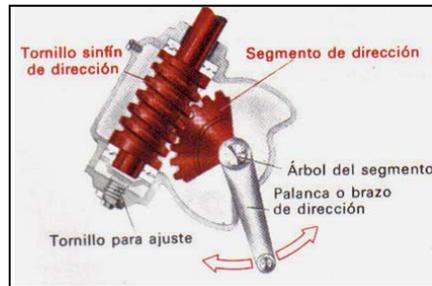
Mecanismo de tornillo sin fin con segmento.
